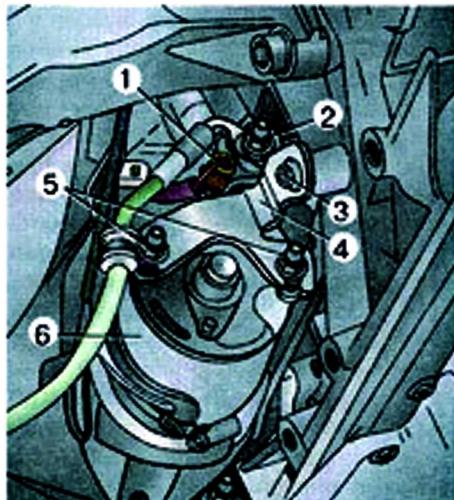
Крепление стартера на двигателе автомобилей Audi 80/90: 1 – вывод +50; 2 – вывод -30; 3 – болт крепления кронштейна стартера; 4 – кронштейн крепления стартера; 5 – гайка крепления стартера к кронштейну; 6 – стартер
